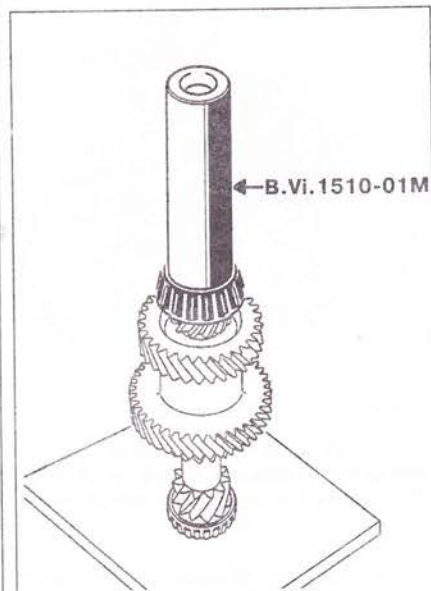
Установите подшипники при помощи приспособления B. Vi. 1510-01, индекс M.
